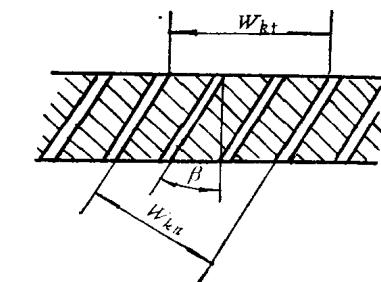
斜齿圆柱齿轮分度圆柱的展开图
